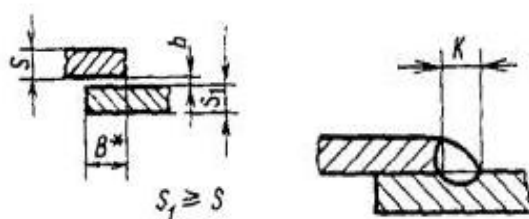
Зовнішній вигляд та підготовка крайок під зварювання з'єднання внапусток Н1
